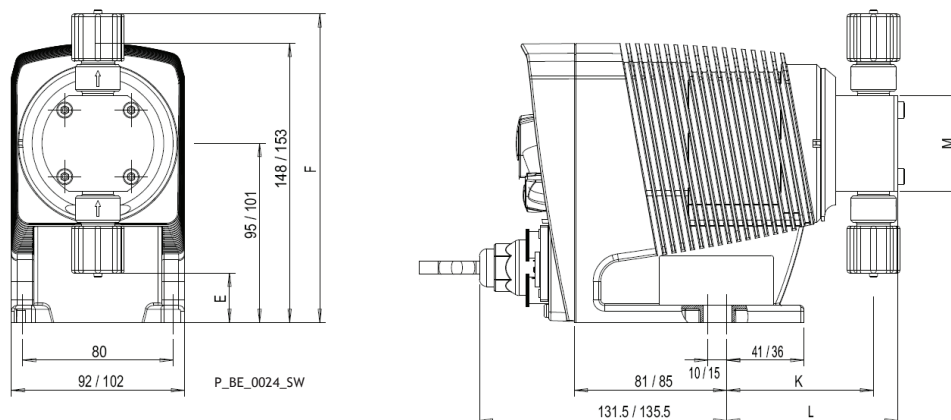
Размерный чертеж Beta® BT4b/BT5b, Материал конструкции ТТ – размеры в мм
